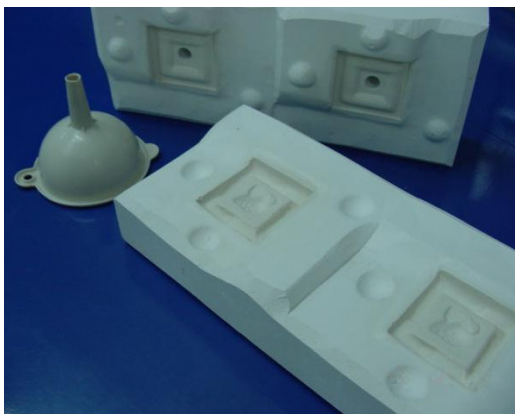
Funil e molde de gesso utilizado para os ensaios.
